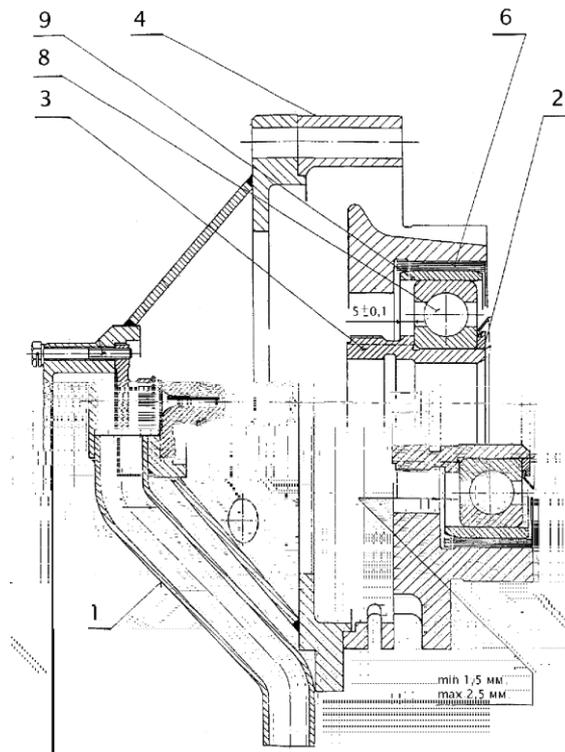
Подшипниковая опора турбины турбокомпрессора PDH50 ZV-D
